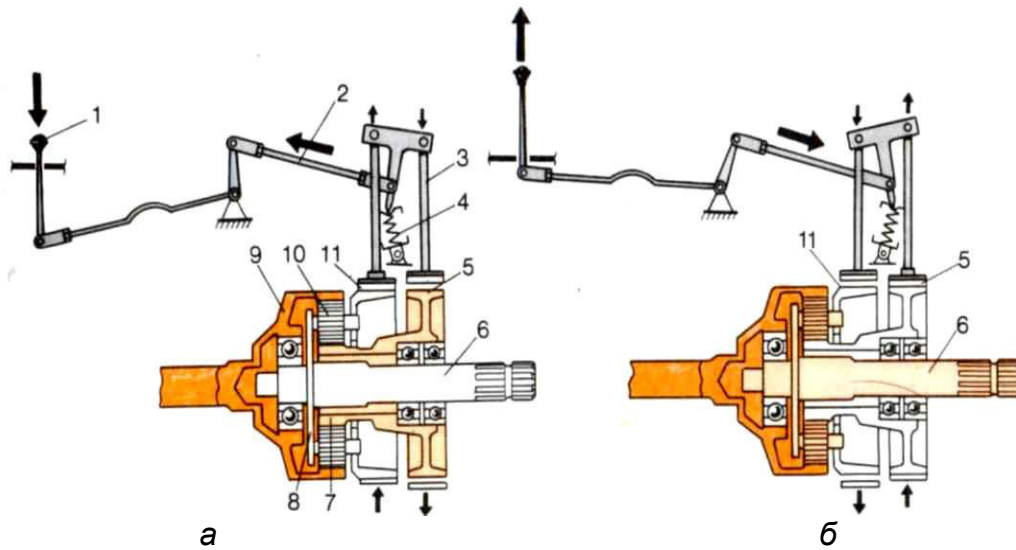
Привод ВОМ трактора МТЗ-82.1: а – планетарный редуктор выключен; б – планетарный редуктор включен
